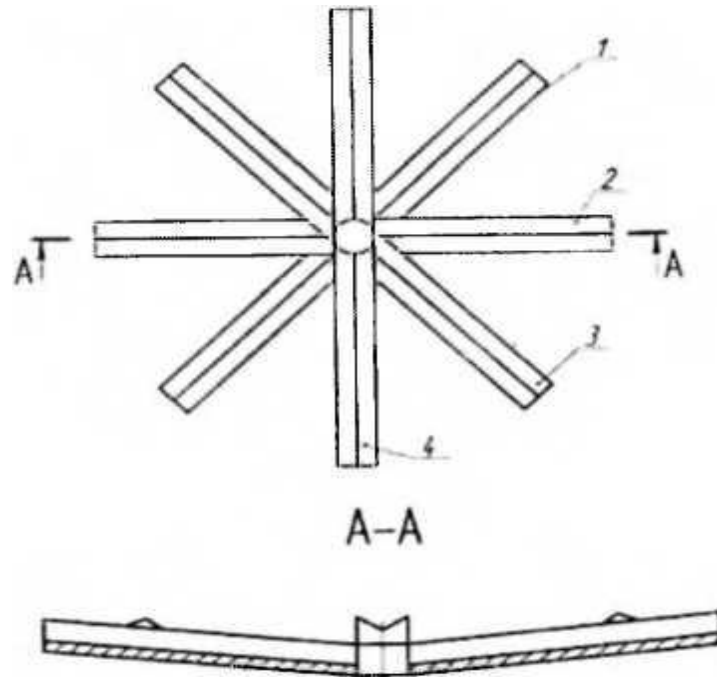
Робочий орган [12], вид зверху і переріз А-А
